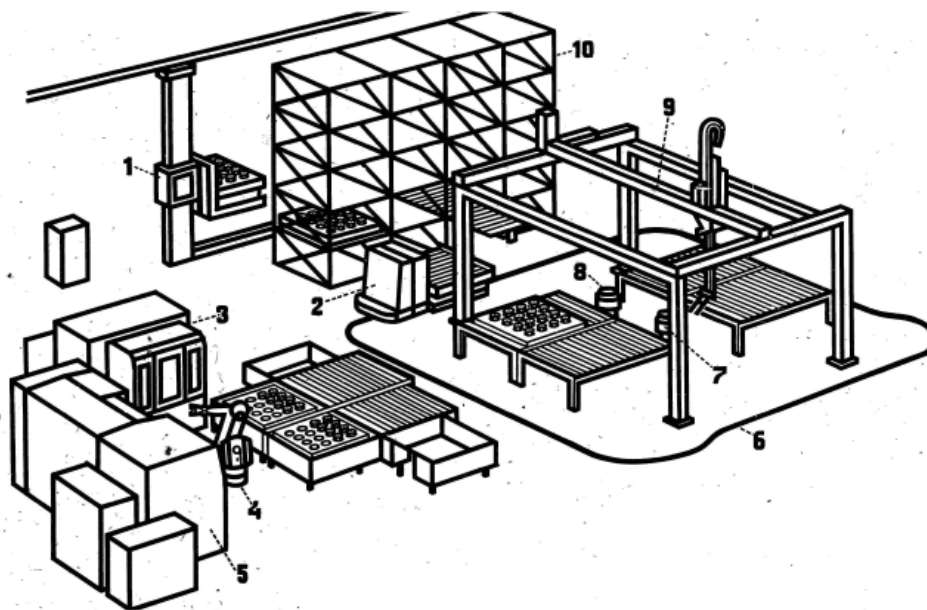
Компоновка ГПС механообработки и сборки [6]
